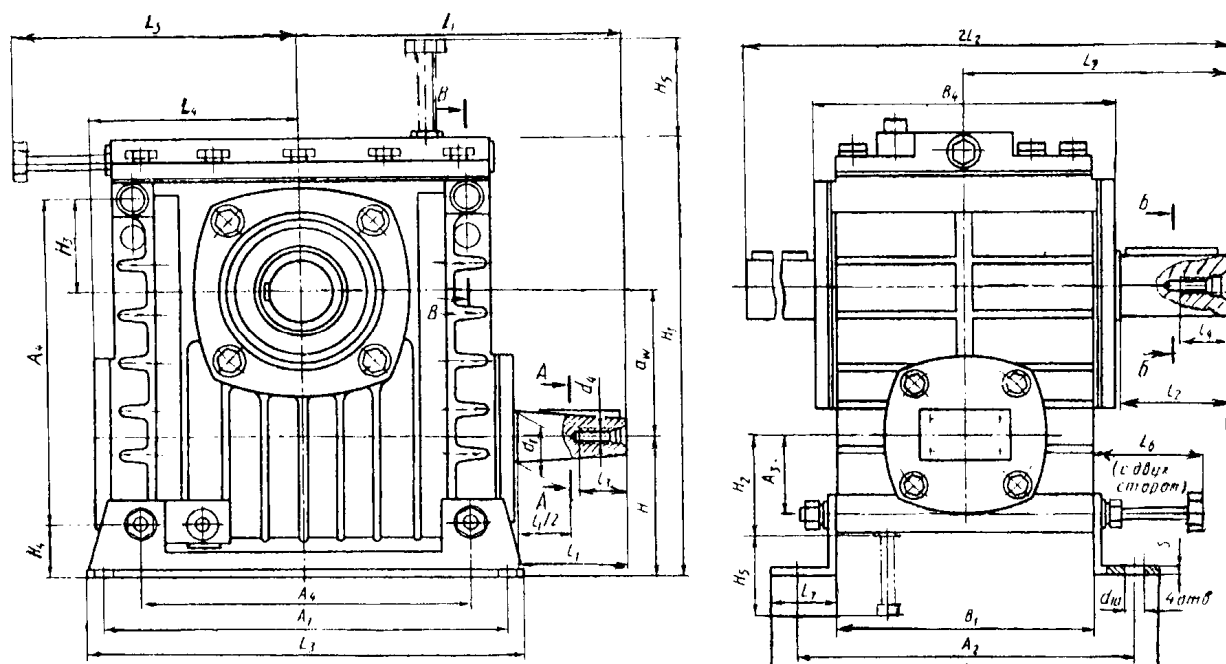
Редуктор червячный одноступенчатый типа 2Ч (a_w 40, 63, 80) ГОСТ27701-88. Колесо опускается в корпус через прямоугольное отверстие верхней крышки, после чего вал тихоходный вставляется в колесо и собирается с двух сторон с подшипниками и их крышками.
